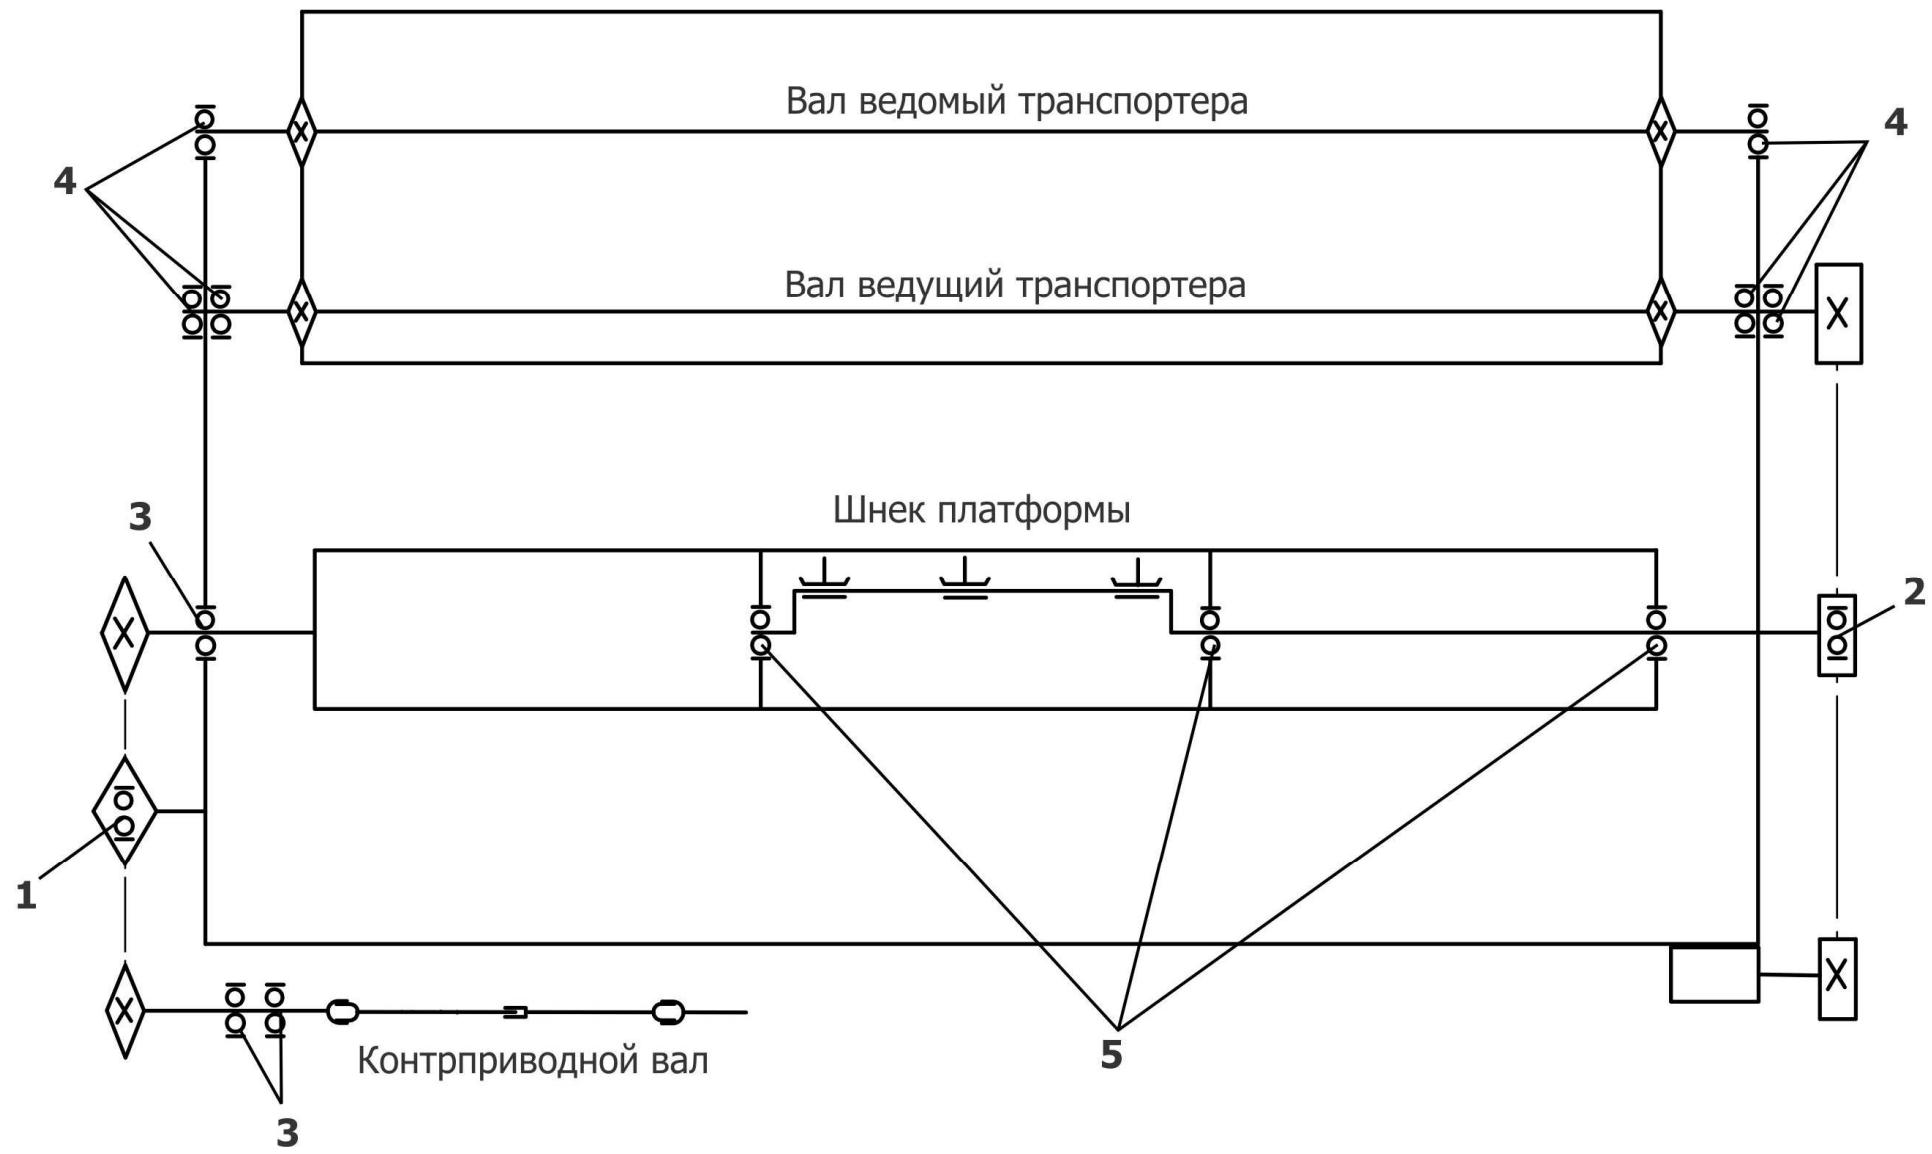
Схема расположения подшипников платформы - подборщика
